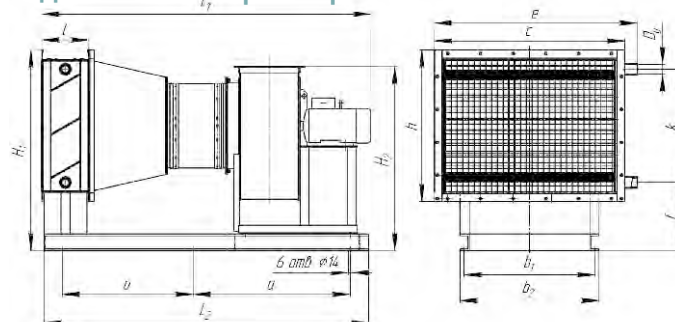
Габаритные и присоединительные размеры воздунонагревательных установок типа ВТУ.
